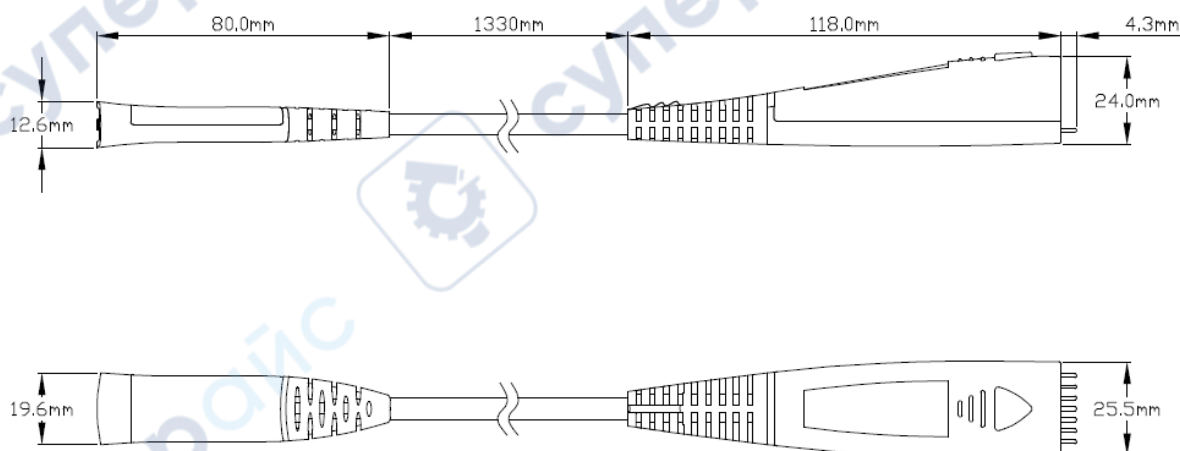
Габаритные размеры пробника, вид сбоку и сверху
